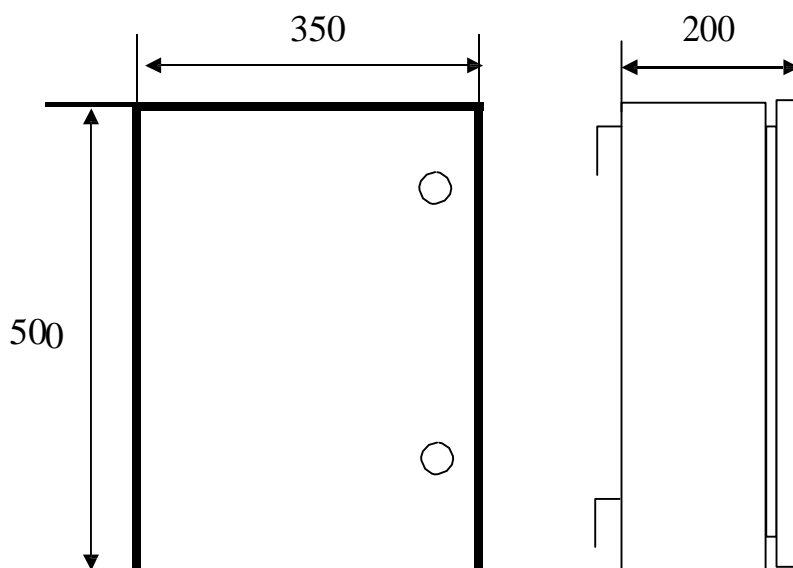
Шкаф низковольтный сбора и передачи данных, аппаратуры РЗА. Общий вид и габаритные размеры.
